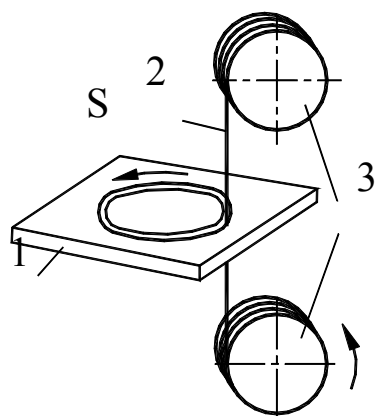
Схема электроискровой обработки проволокой: 1 – заготовка; 2 – проволока; 3 – катушки с проволокой; S – направление рабочей подачи
